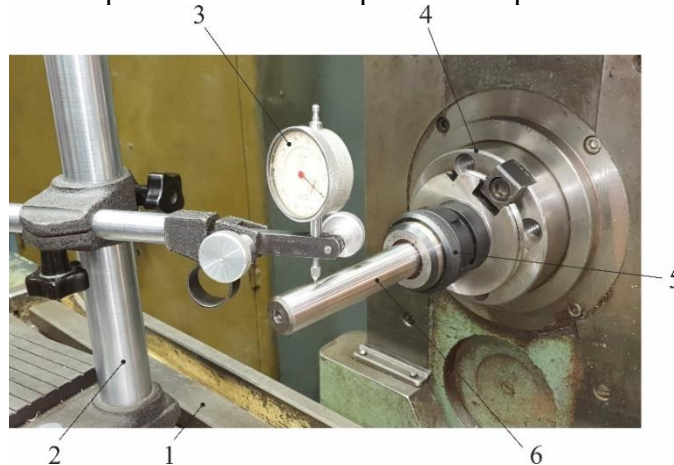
Измерение биения: 1 - стол станка; 2 - индикаторная стойка; 3 - индикатор; 4 - шпиндель станка; 5 - цанговый патрон; 6 - контрольная оправка.
